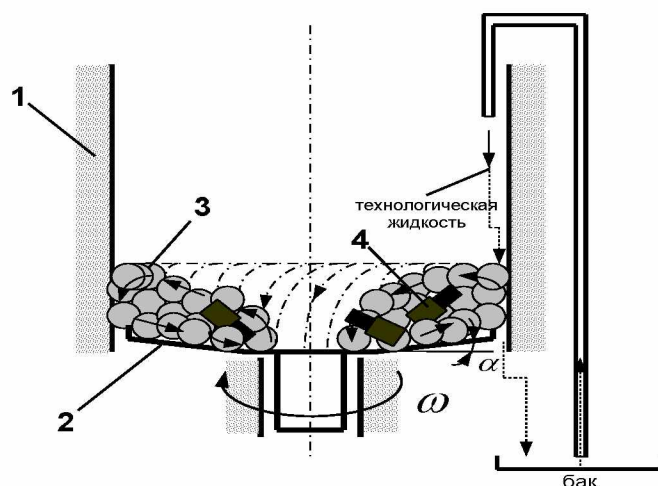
Схема процесу відцентрово-ротаційної обробки
